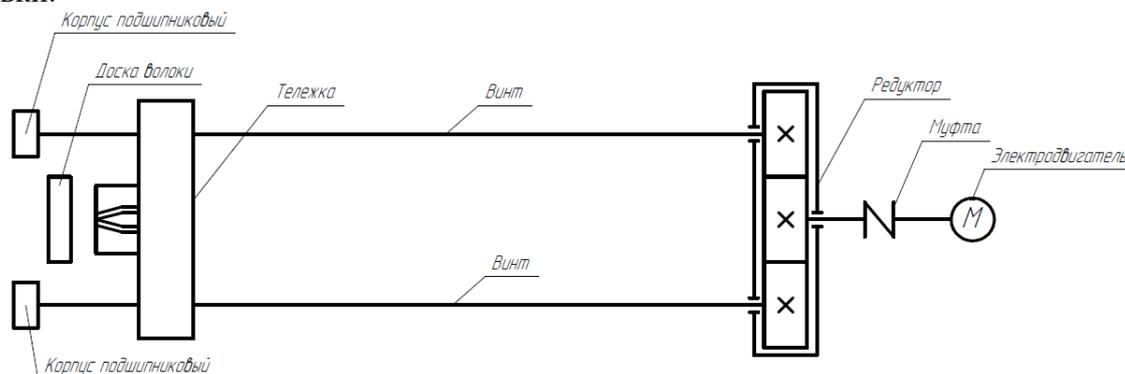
Кинематическая схема двухвинтового привода лабораторного стана
